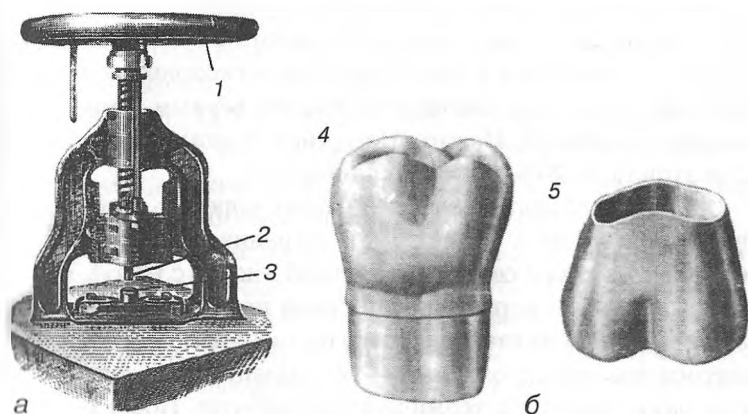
Пресс для наружной штамповки коронки (а) и готовая коронка (б):
